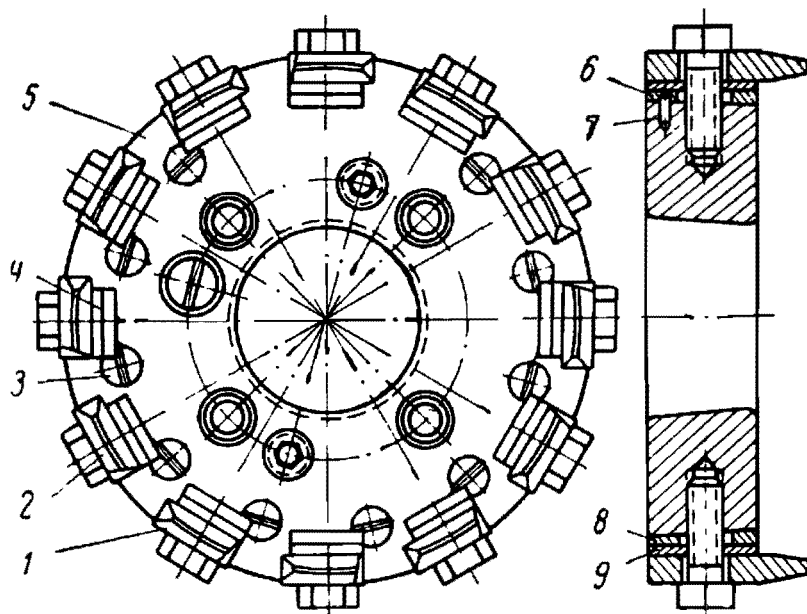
Зуборезная праворежущая сборная резцовая головка для нарезания круговых зубьев конических колес
